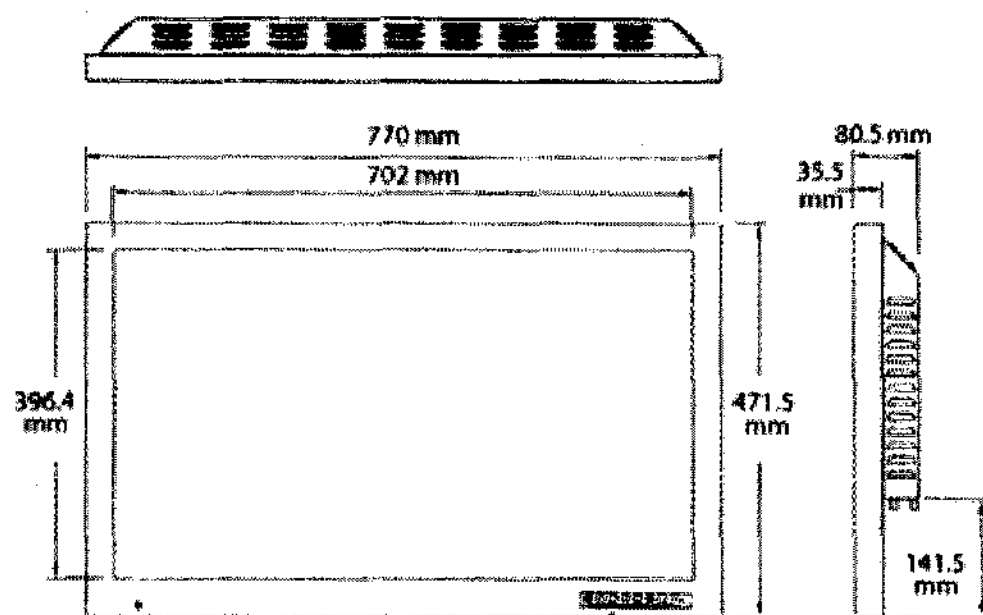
Габаритный чертеж Мониторов FS-P3102D и FS-P3102DS
